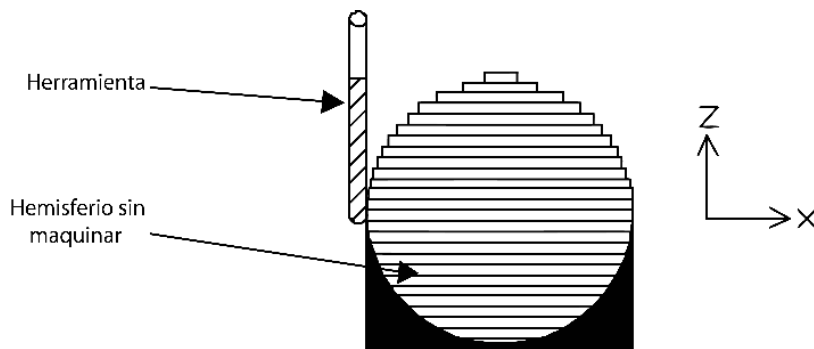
Ilustración esquemática del maquinado de una esfera mediante CNC-RP, [205]
